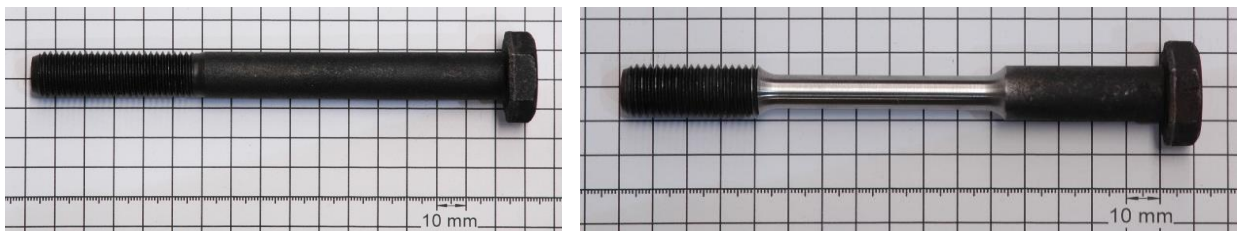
Proben für den Zugversuch: fertige HV-Schraube M16 (links) und abgedrehte Probe aus HV-Schraube M16 (rechts)
